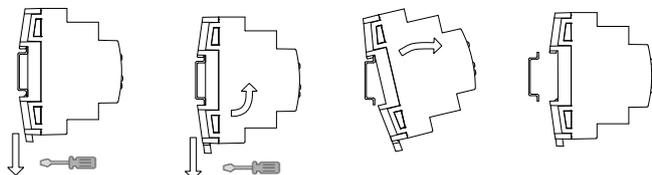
Montaje de FANinBOX 110V 1CH en carril DIN
